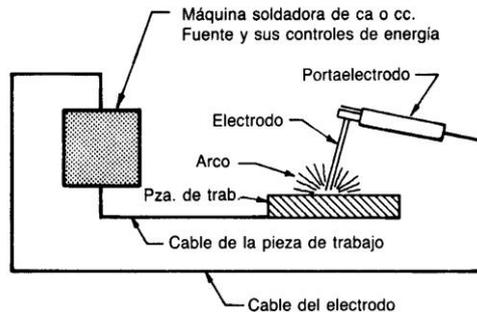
Esquema de soldadura por arco eléctrico
